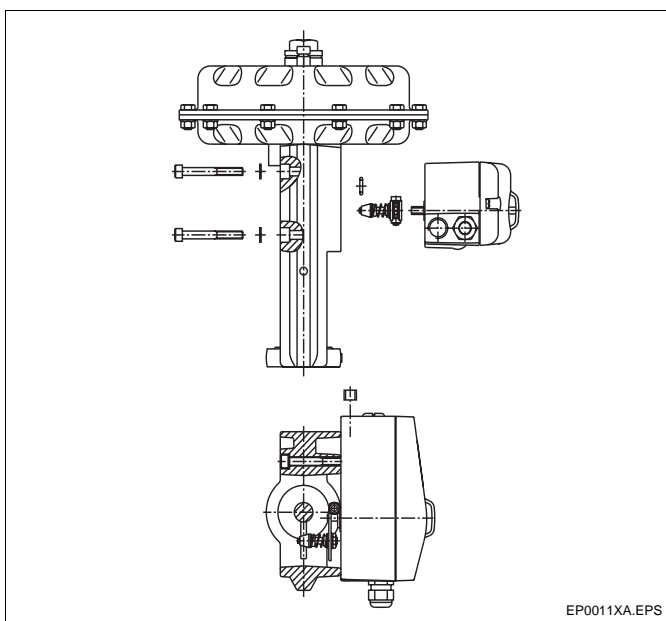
Montage intégré sur vannes de réglage 23/24 et 23/25
